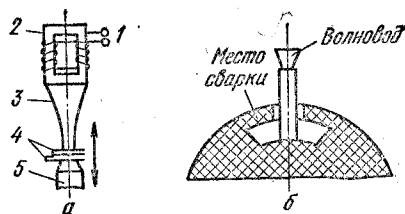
Схема ультразвуковой сварки: 1 — обмотка; 2 — магнитно-стрикционный преобразователь; 3 — волновод; 4 — свариваемое изделие; 5 — опора
